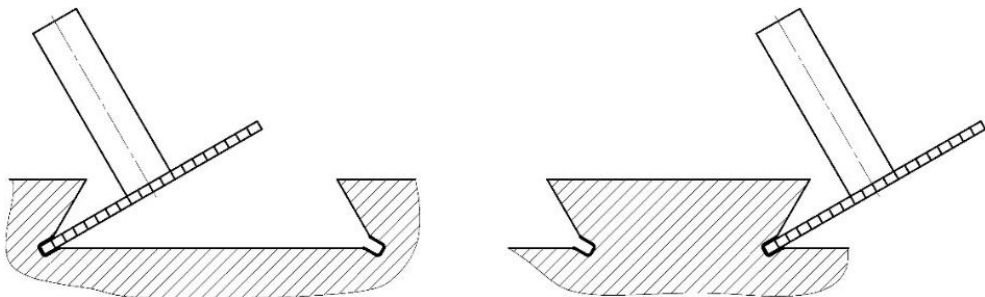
Фрезерування пазу для виходу шліфувального
